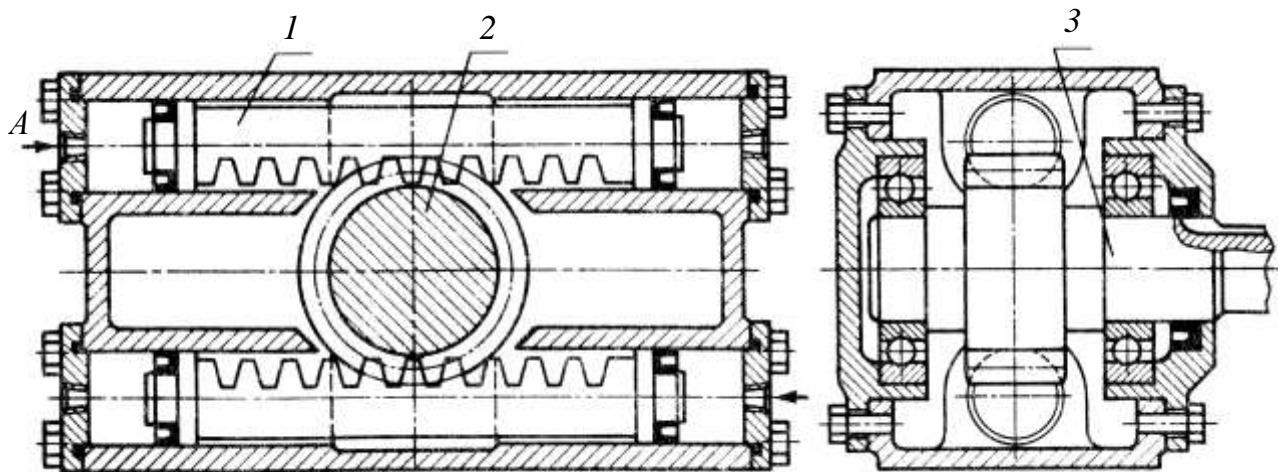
Плунжерный гидроцилиндр с реечной зубчатой передачей
